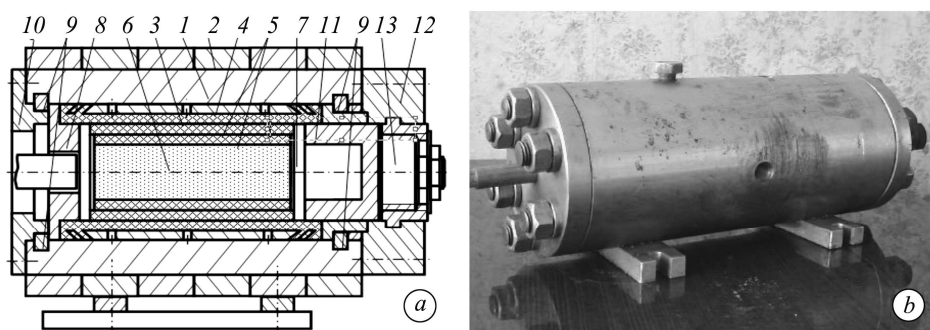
Схема конструкції (а) та загальний вид (b) прес-блока напівпромислової установки для СР-ІІІ у замкнутому об'ємі: 1 – корпус; 2 – кільця (бандаж); 3 – вкладиш еластичний; 4 – армувальний елемент; 5 – набір оболонок еластичних; 6 – порошок; 7 – пробка; 8 – упорний диск; 9 – кулачки розрізні; 10, 12 – кришки; 11 – стакан; 13 – повзун.
